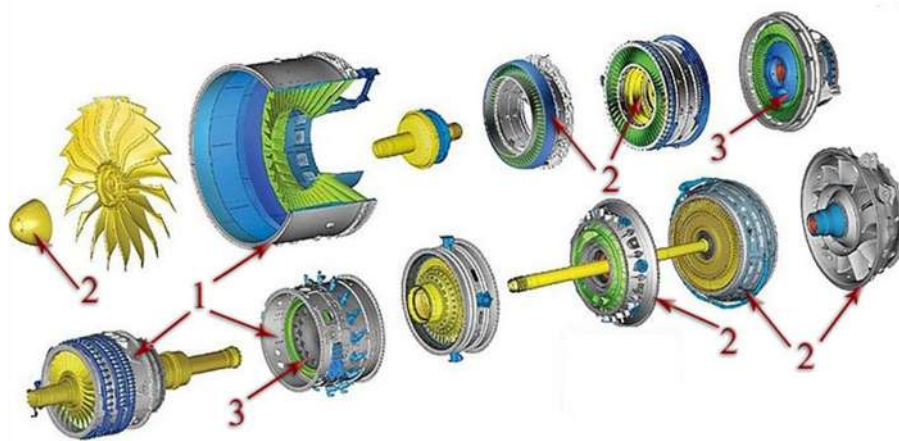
Класифікація деталей двигуна і форм заготовок для штампування [15]: 1 – циліндрична; 2 – конічна; 3 – плоска
